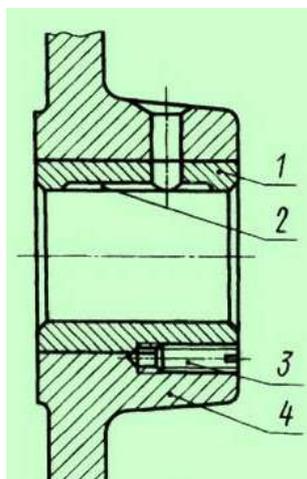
Неразъемный подшипник, встроенный в станину машины:
